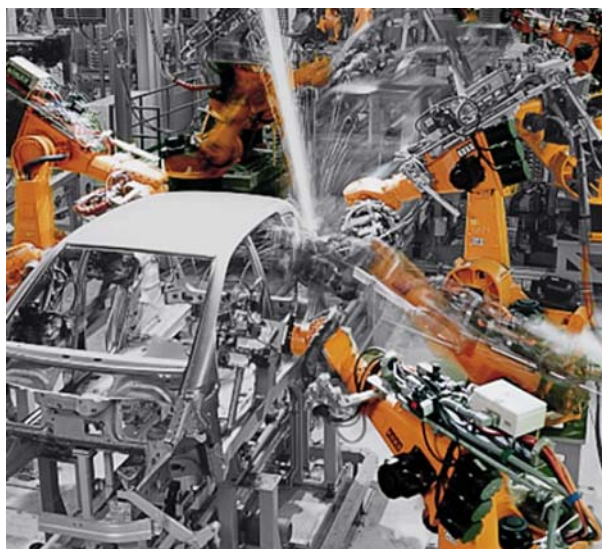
Точечная сварка неотделанного кузова
